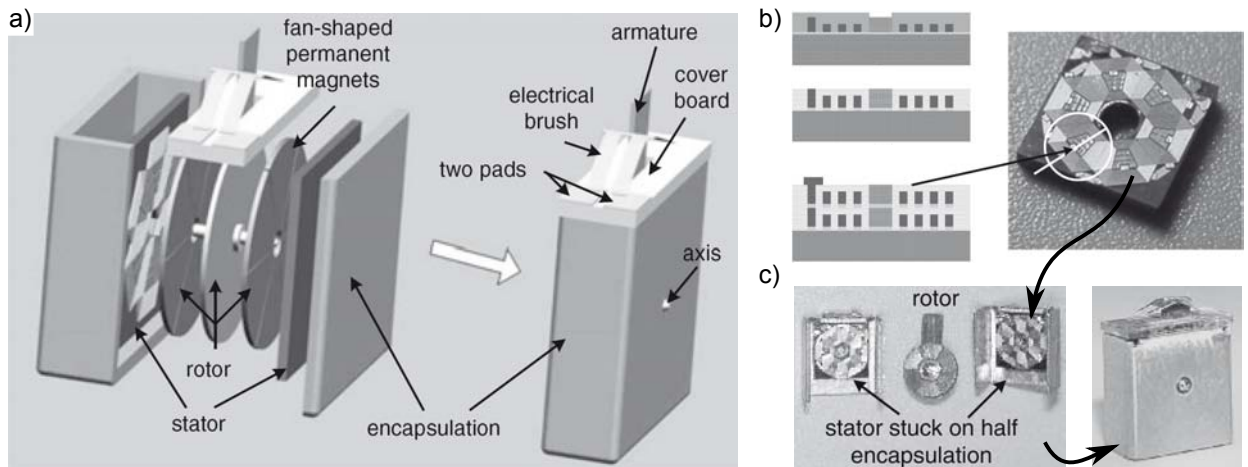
Elektrodynamisches Mikrorelais mit mikrotechnischen Anteilen und komplexer Endmontage: a) CAD-Explosionszeichnung des Systemaufbaus bestehend aus Gehäuse, Stator mit Flachspulen, Rotor mit Permanentmagneten und mechanisch bistabiles elektrisches Kontaktsystem, b) schematischer Querschnitt und Foto des Stators und c) Fotos vom vereinfachten Montagevorgang zum finalen Relais [157].
